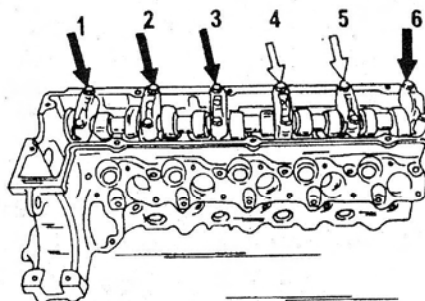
Ослабление крепления крышек подшипников пятицилиндрового двигателя. Крышки, помеченные черными стрелками, отвернуть, крепление крышек, помеченных белыми стрелками, попеременно перекрестно ослабить.
